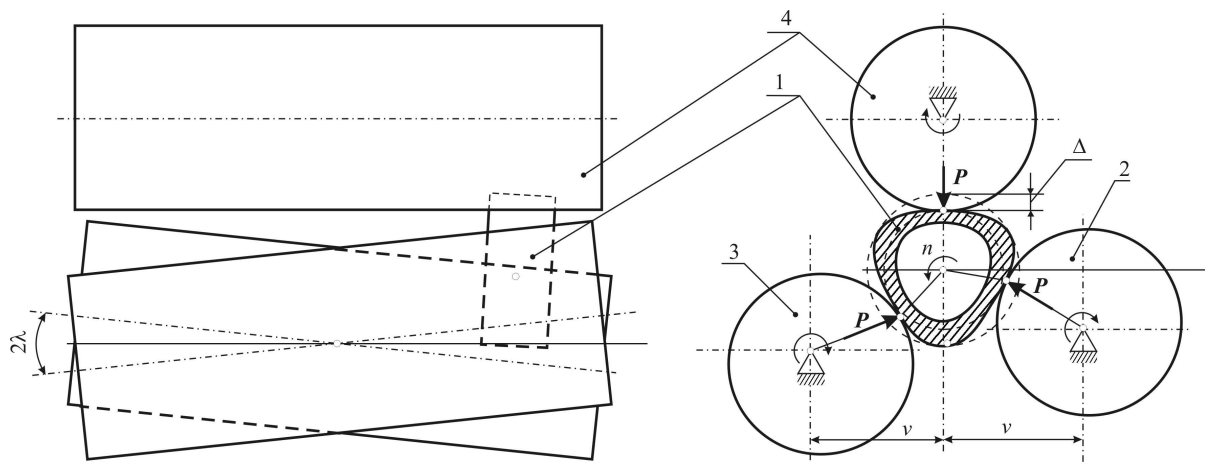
Схема бесцентровой обкатки колец: 1 - кольцо; 2, 3 - базировочные валки; 4 - прижимающий валок
